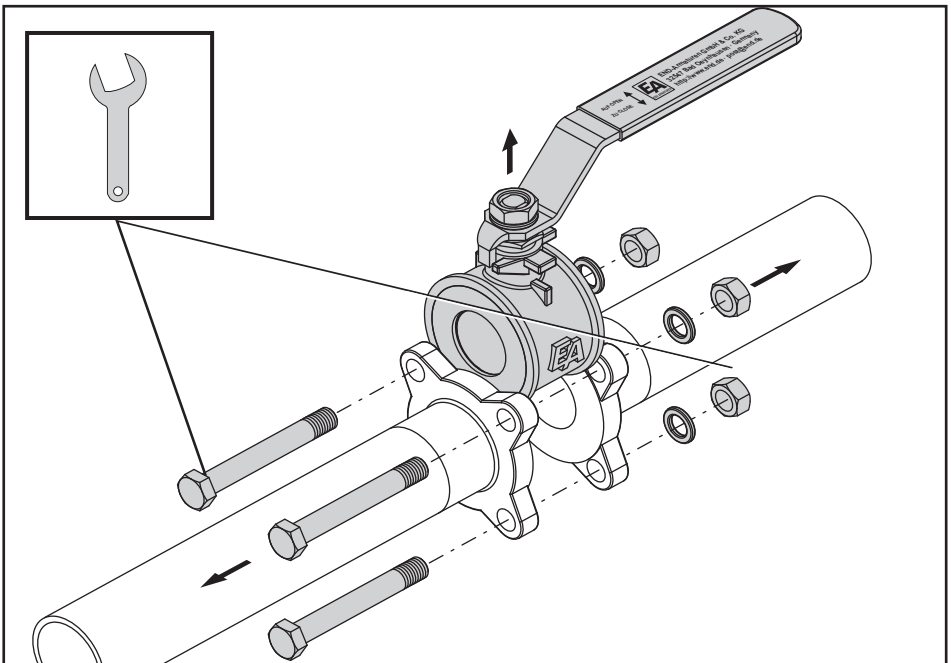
Kugelhähne, Wechslen der Kugel und des Dichtungssatzes: Ausbauen des Kugelhahnmittelteiles (Abbildung zeigt Art. ZE311064)
